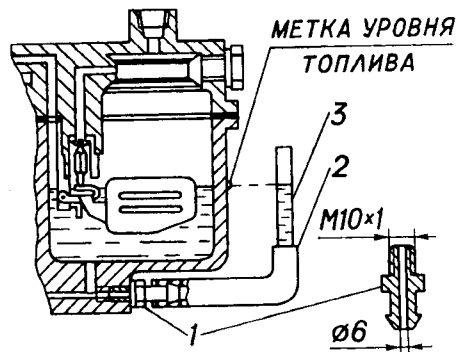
Схема проверки уровня топлива в поплавковой камере:
